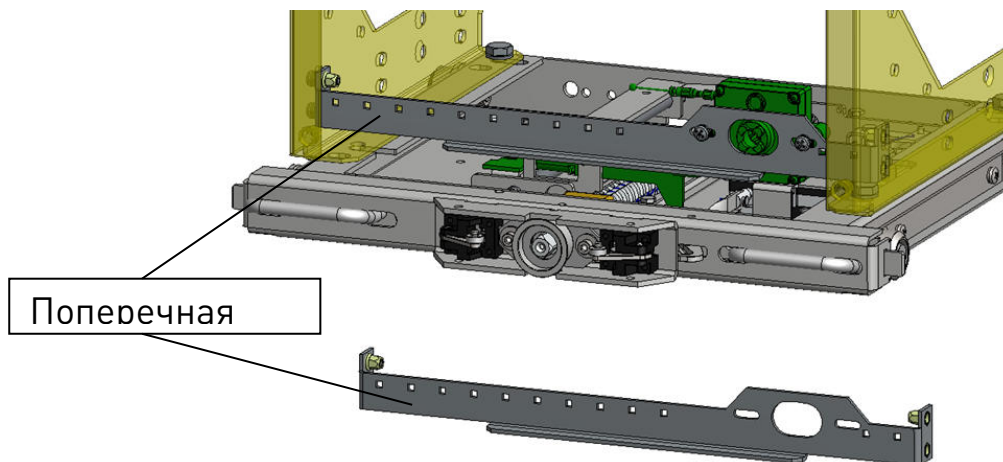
Сборка блокиратора (1 м) КВЭ
